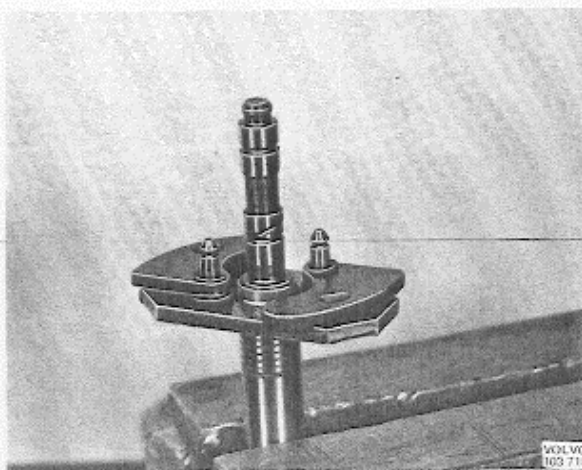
Verteilerwelle mit Fliehgewichten
